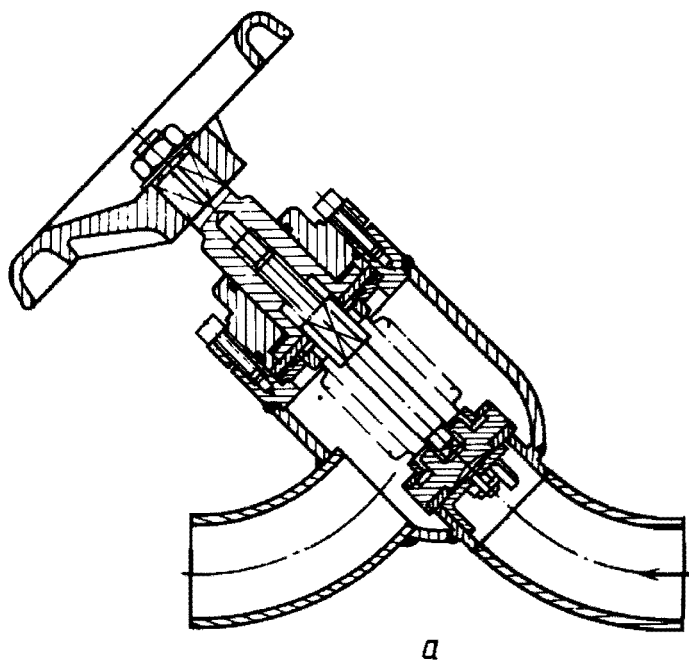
Сильфонный запорный вентиль в сварном корпусе и с концами под приварку (VEB MAW Armaturenwerk, ГДР, Пренцлау):
